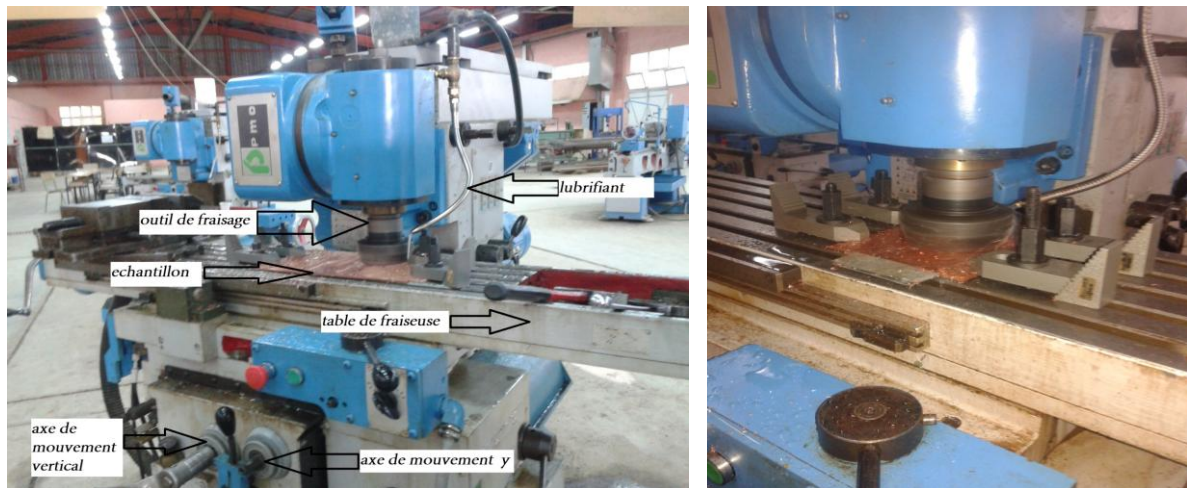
Fraiseuse universelle : usinage des échantillons.
